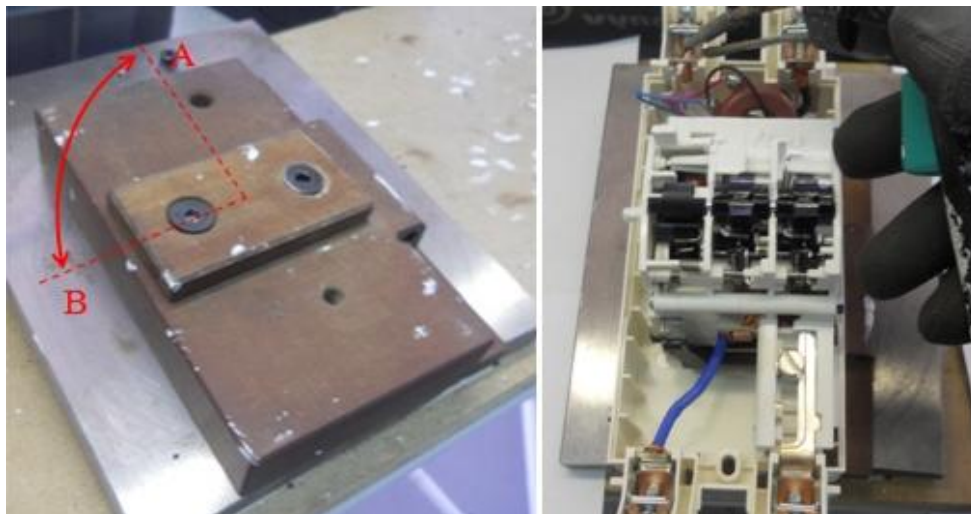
JIG de soldadura do terminal, relê e resistência.
